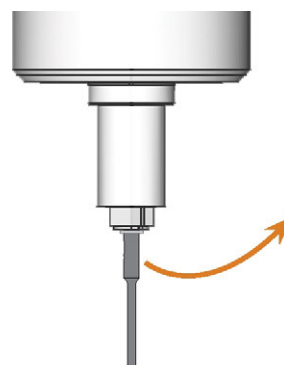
RETIRER L'OUTIL DE LA PINCE DE SERRAGE
